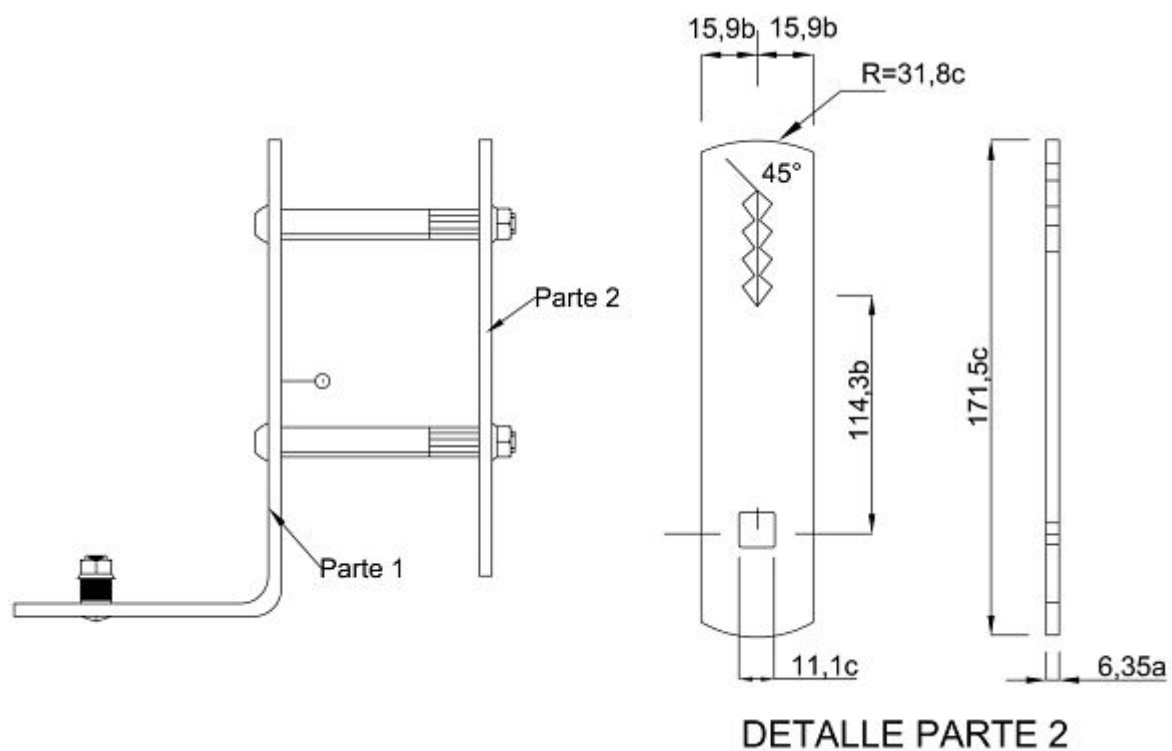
B: Soporte para fijación a cruceta, detalle parte 2. Dimensiones en milímetros [mm]
